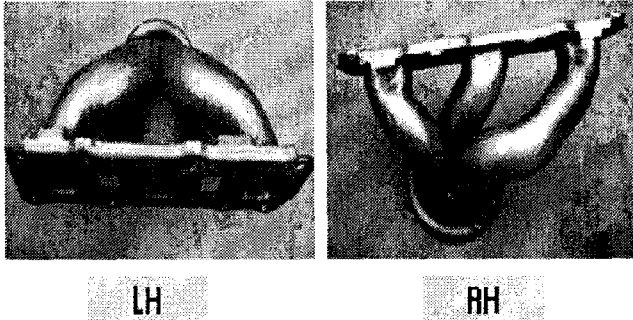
하이드로포밍 배기 매니폴드 Assembly
